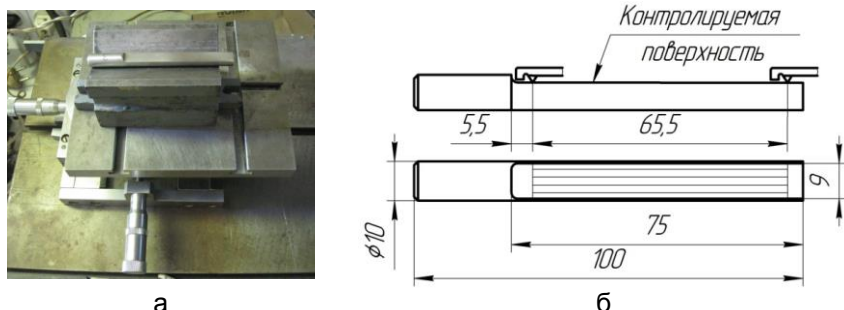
Измерение шероховатости поверхности обрабатываемых деталей: а – общий вид; б – схема измерения
